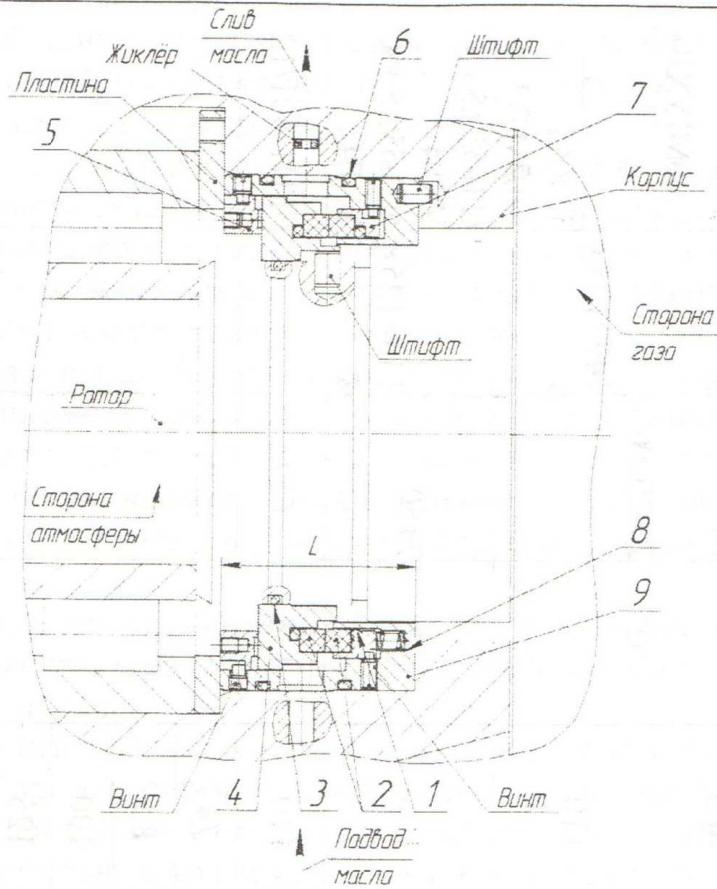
Уплотнение пакетного типа для винтового компрессора: 1,3,6 - кольцо резиновое; 2 - кольцо уплотнительное (пара трения); 4 - втулка; 5 - подпятник; 7 - кольцо нажимное; 8 - пружина; 9 - корпус
